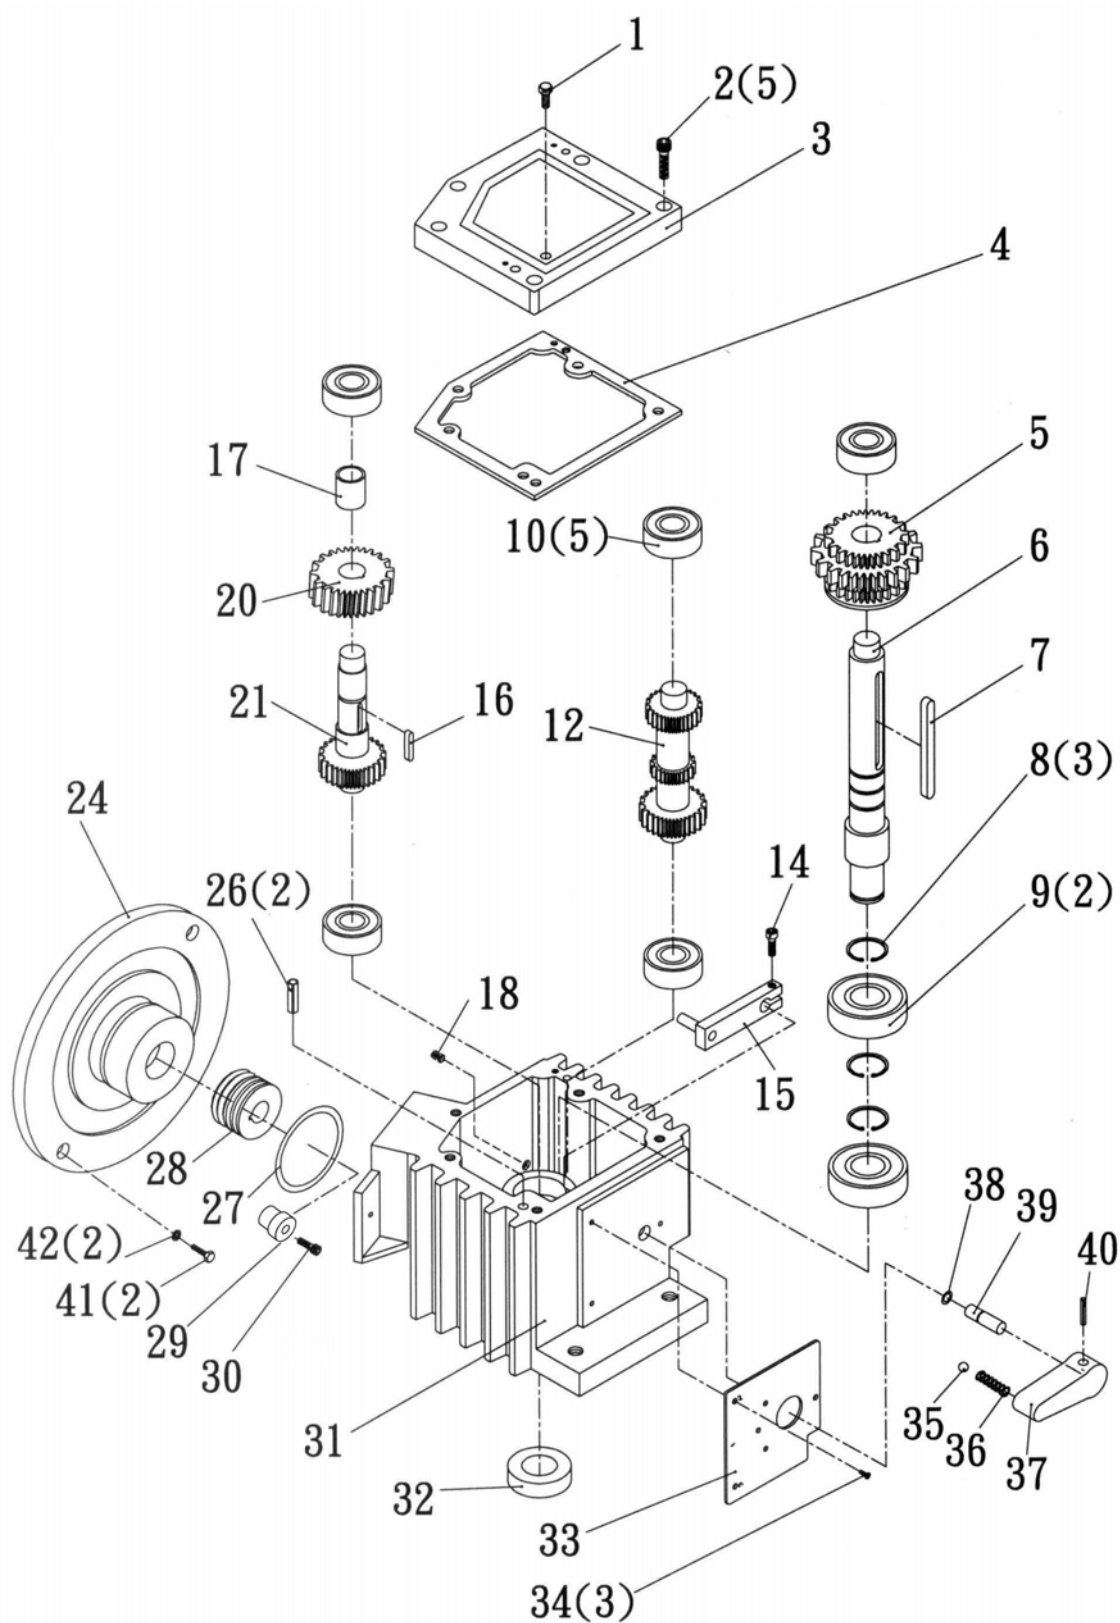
Explosionszeichnung Getriebe - Equipo de dibujo de explosión: 712AGN segunda generación
